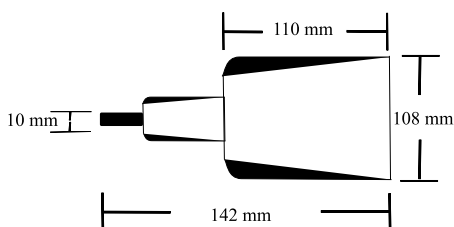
Dimensiones físicas del motor Turnigy Rotomax 80cc
